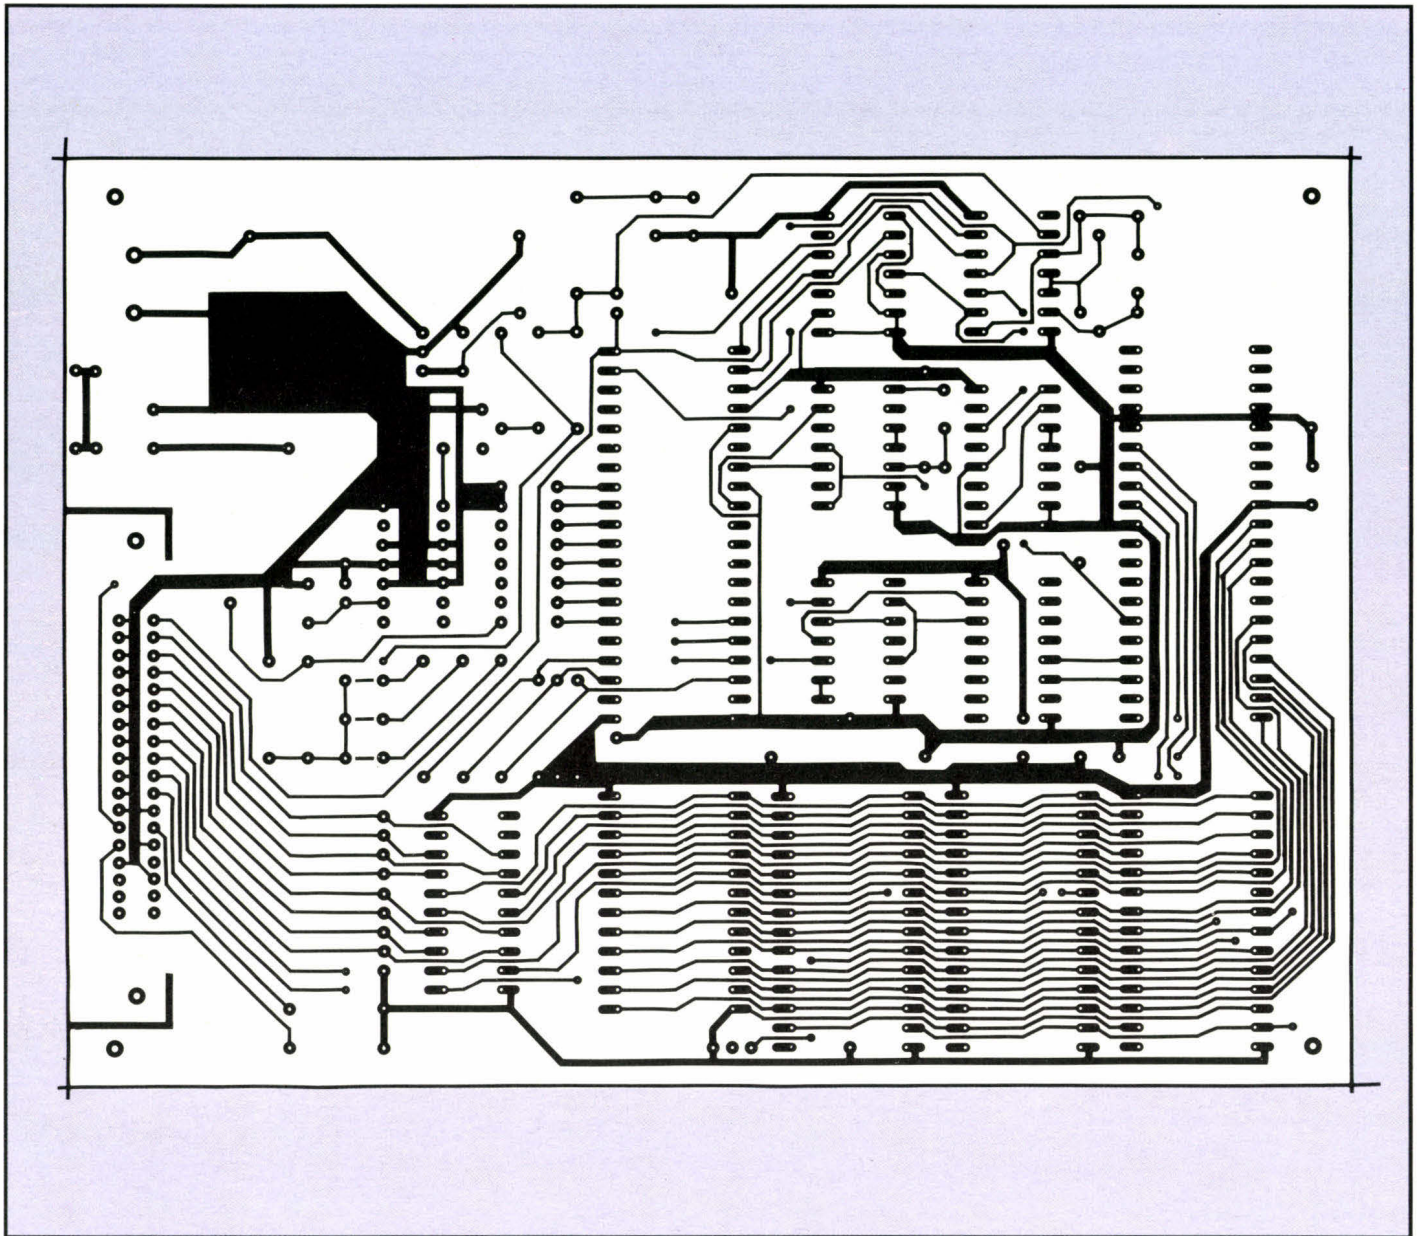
a) Circuit imprimé vu côté soudures.
